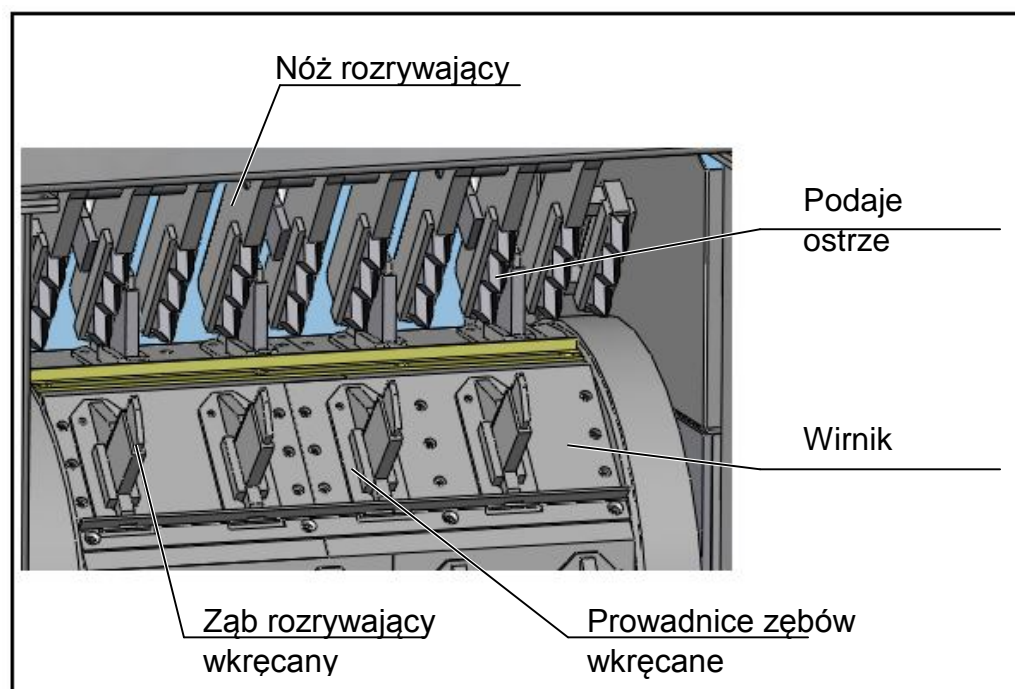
pokazuje maszynę do rozrywania worków. Konstrukcja podstawowych elementów maszyny została opisana poniżej.
